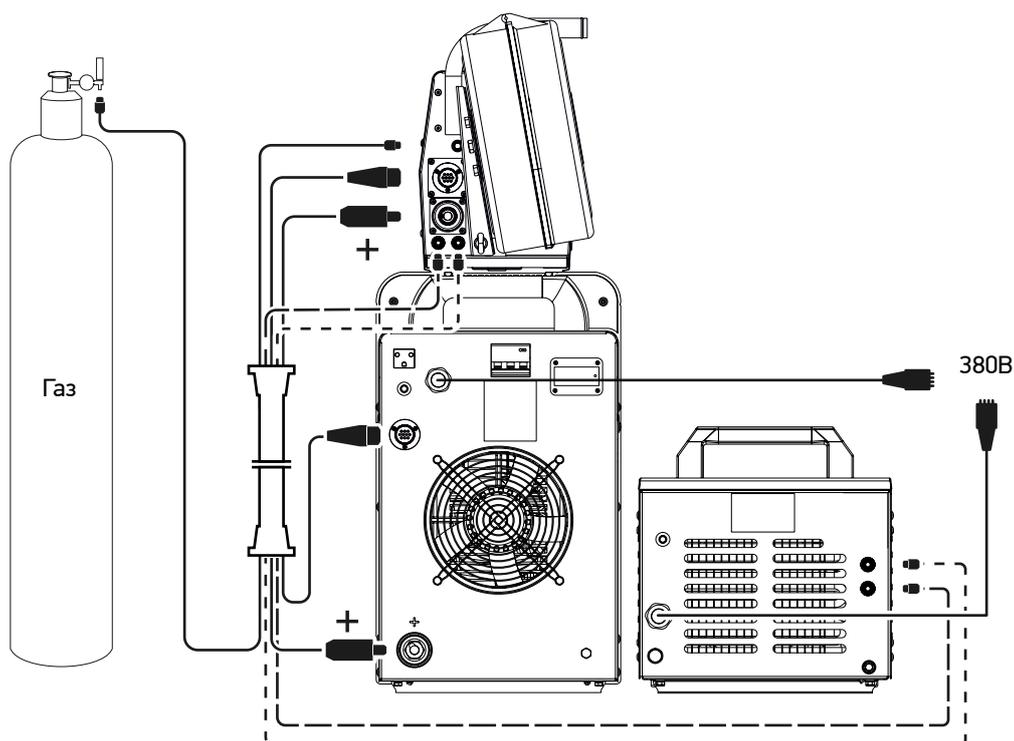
Схема соединений комплекта сварочного оборудования TIG
